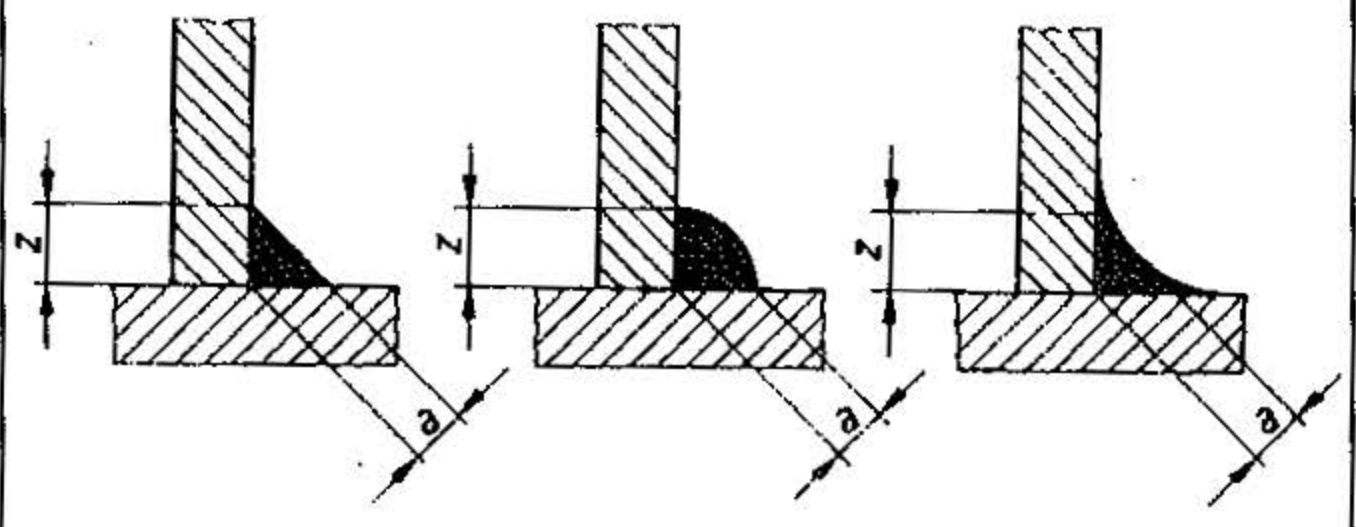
Métodos para indicar dimensiones en las soldaduras
